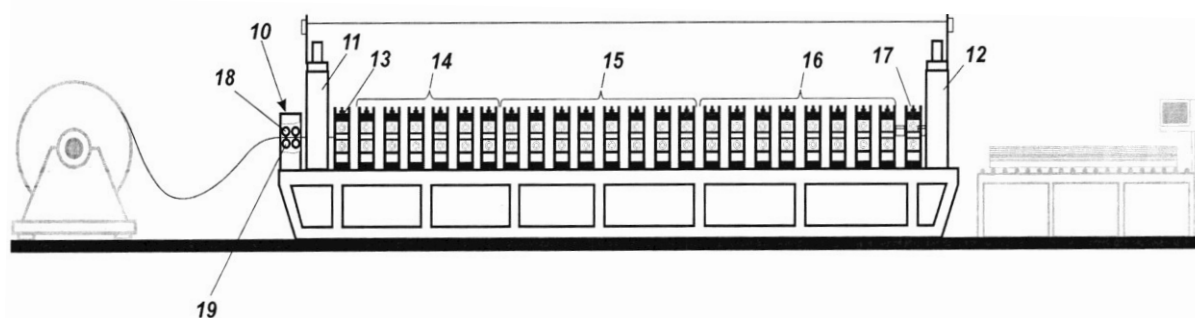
Многоклетьевого профилегибочный стан изготовления профиля (общий вид) [6, с. 56]:
